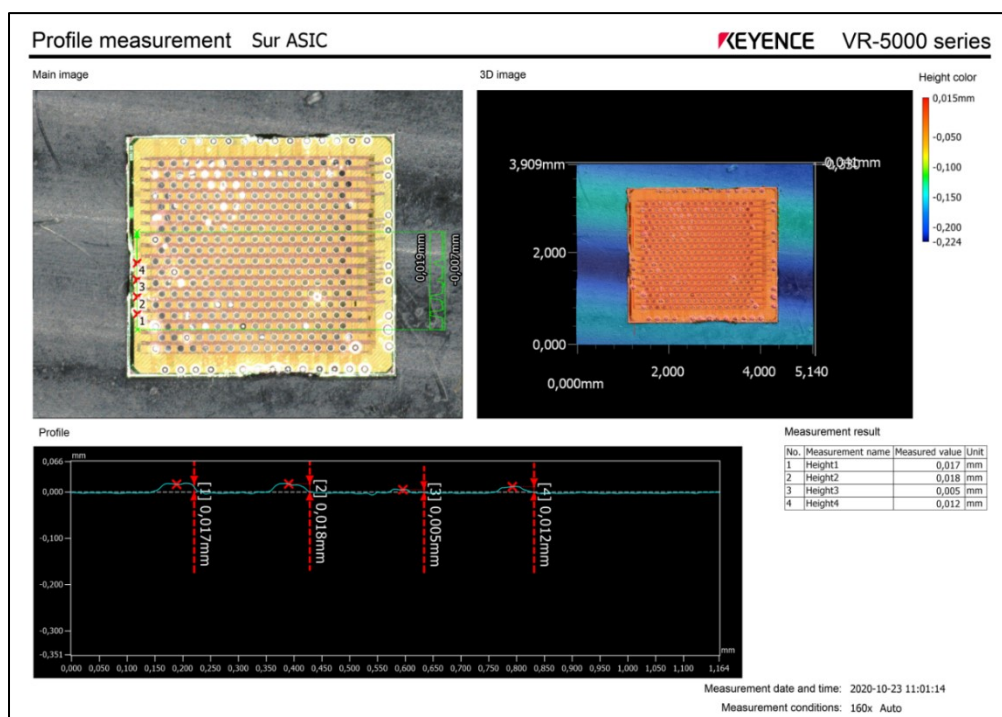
Vue des *solderbumps* sur l'ASIC après la tentative d'assemblage de l'ASIC
